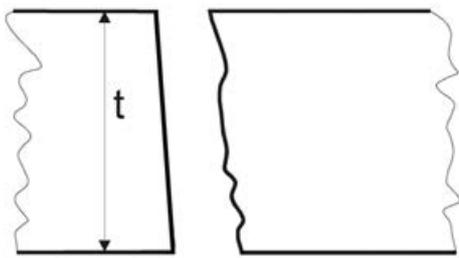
Stoßflächenvorbereitung beim Felgenschweißen durch Schnitt mit einem Schnittwerkzeug und Biegen des Blechabschnitts zum Ring – gut geeignet.
